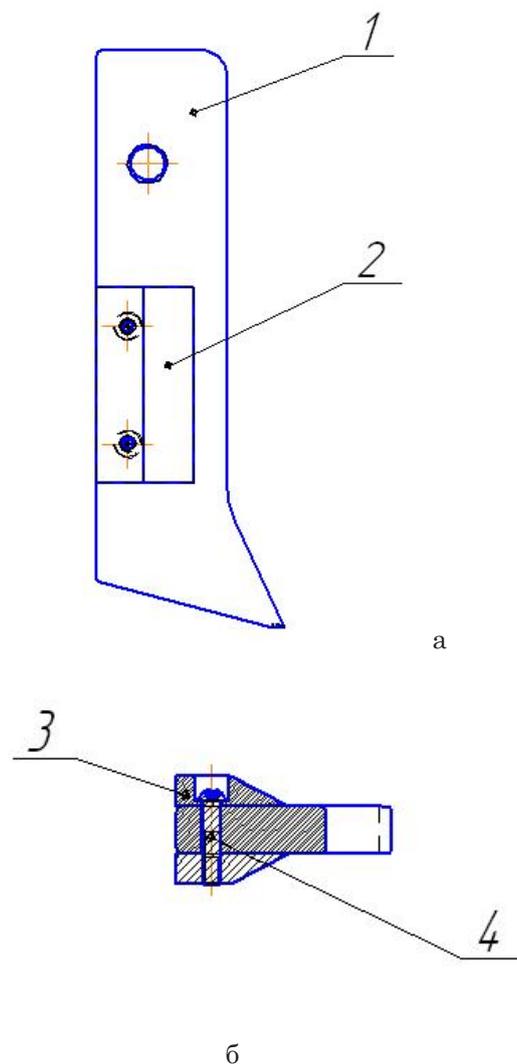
Сошник сборной конструкции с болтовыми соединениями:
